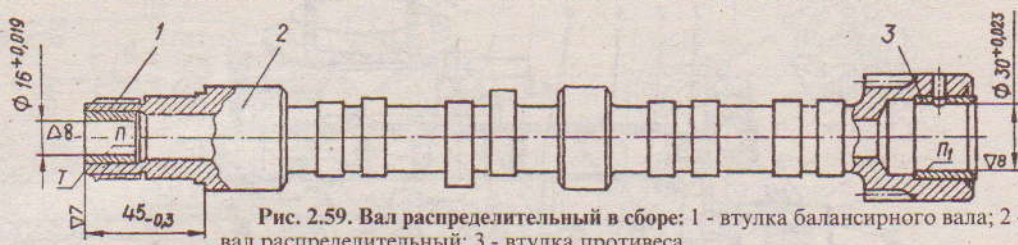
Вал распределительный в сборе: 1 - втулка балансирующего вала; 2 - вал распределительный; 3 - втулка противовеса
